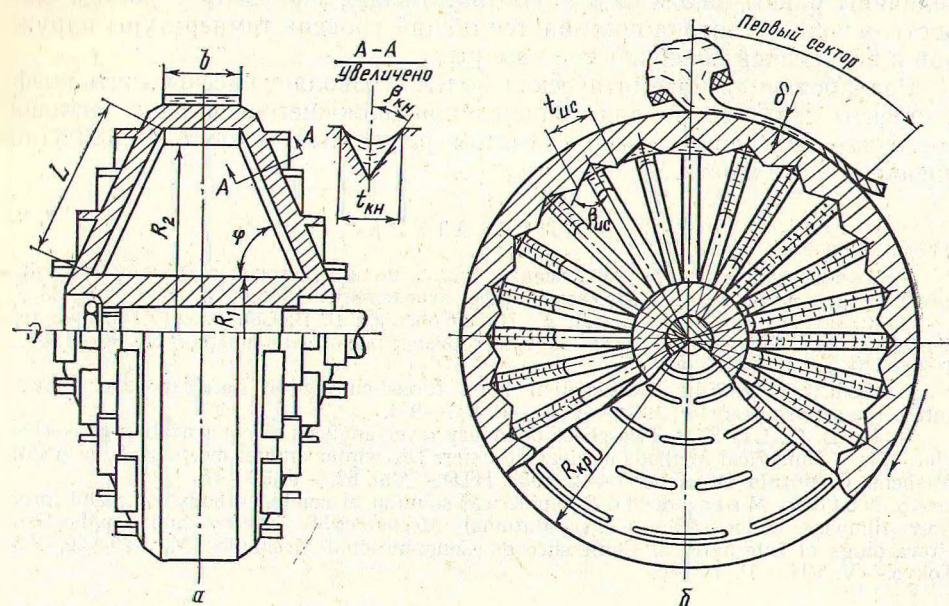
Схема кристаллизатора для получения металлической ленты методом быстрого охлаждения из жидкого состояния: а — фронтальный вид; б — сбоку
